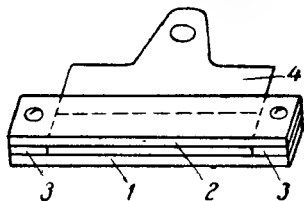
Приспособление для отбортовки манжеты пазовой коробочки.
